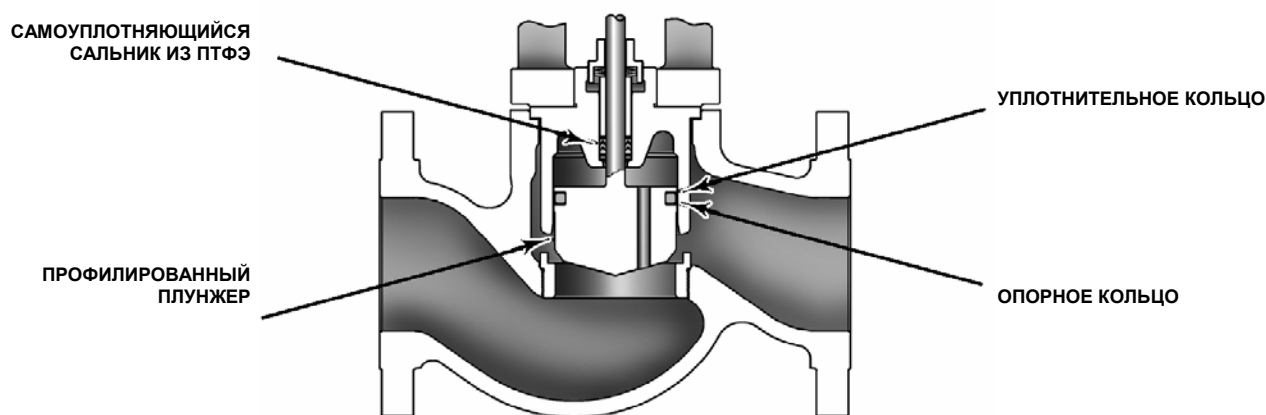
Регулирующий клапан конструкции GX с разгруженным плунжером (только для размеров порта 70, 90 и 136).
